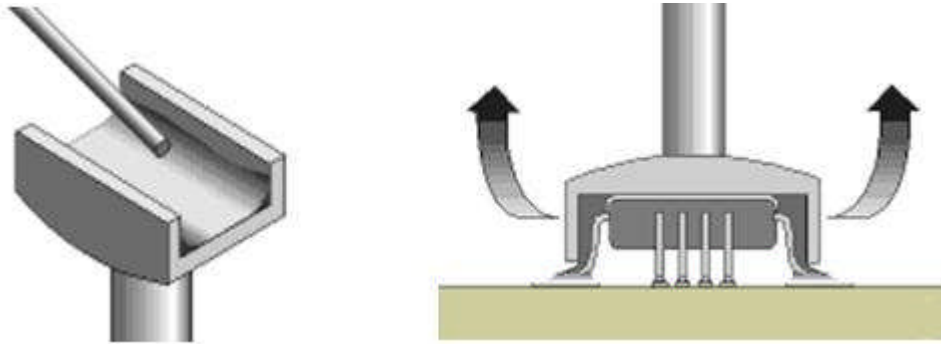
Solder-light kullanarak yüzey montaj entegrelerin lehimlenmesi
